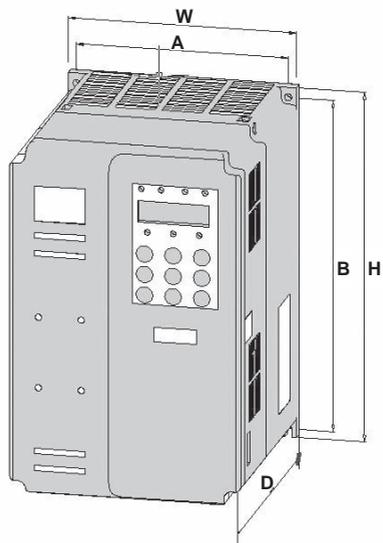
Внешний вид и тип монтажа преобразователя частоты в пластиковом корпусе
